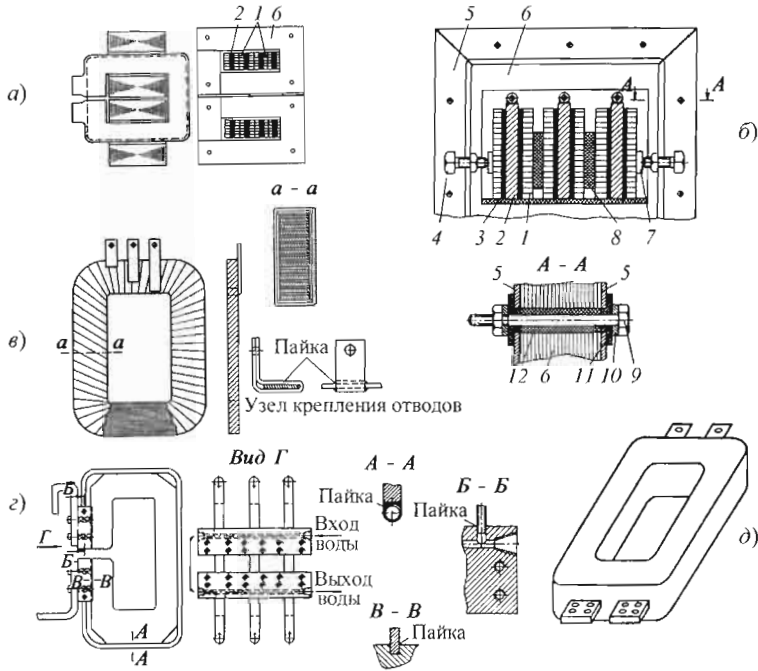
Конструктивная схема (а) и компоновка (б) обмоток сварочного трансформатора броневого типа; конструкция дисковой катушки первичной обмотки (в) и плоских секций вторичного витка (г); блок обмоток, залитых эпоксидным компаундом (д):
